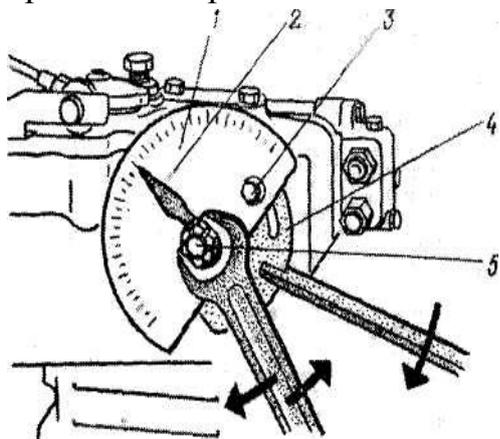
2. Регулировка зазора в зацеплении червяк-сектор поворотом регулировочной втулки: 1 — лимб; 2 — стрелка-указатель; 3 — стопорный болт; 4 — регулировочная втулка червяка; 5 — червяк
